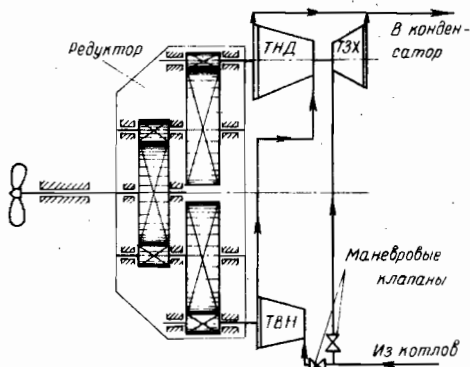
Схема ГТЗА с двухкорпусной турбиной и двухступенчатым зубчатым редуктором
